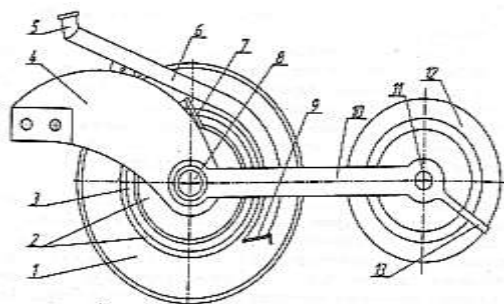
Комбинированный однодисковый сошник с двухсторонними ребордами-бороздкообразователями и нулевым углом атаки дисков:
